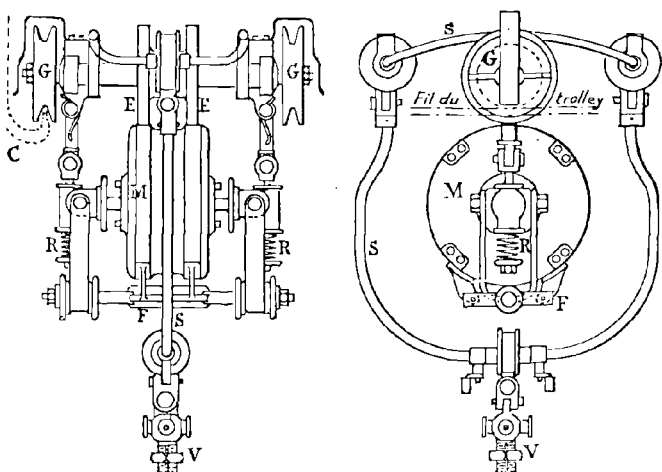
Trolley automoteur. — Vue de face. — Vue latérale.
